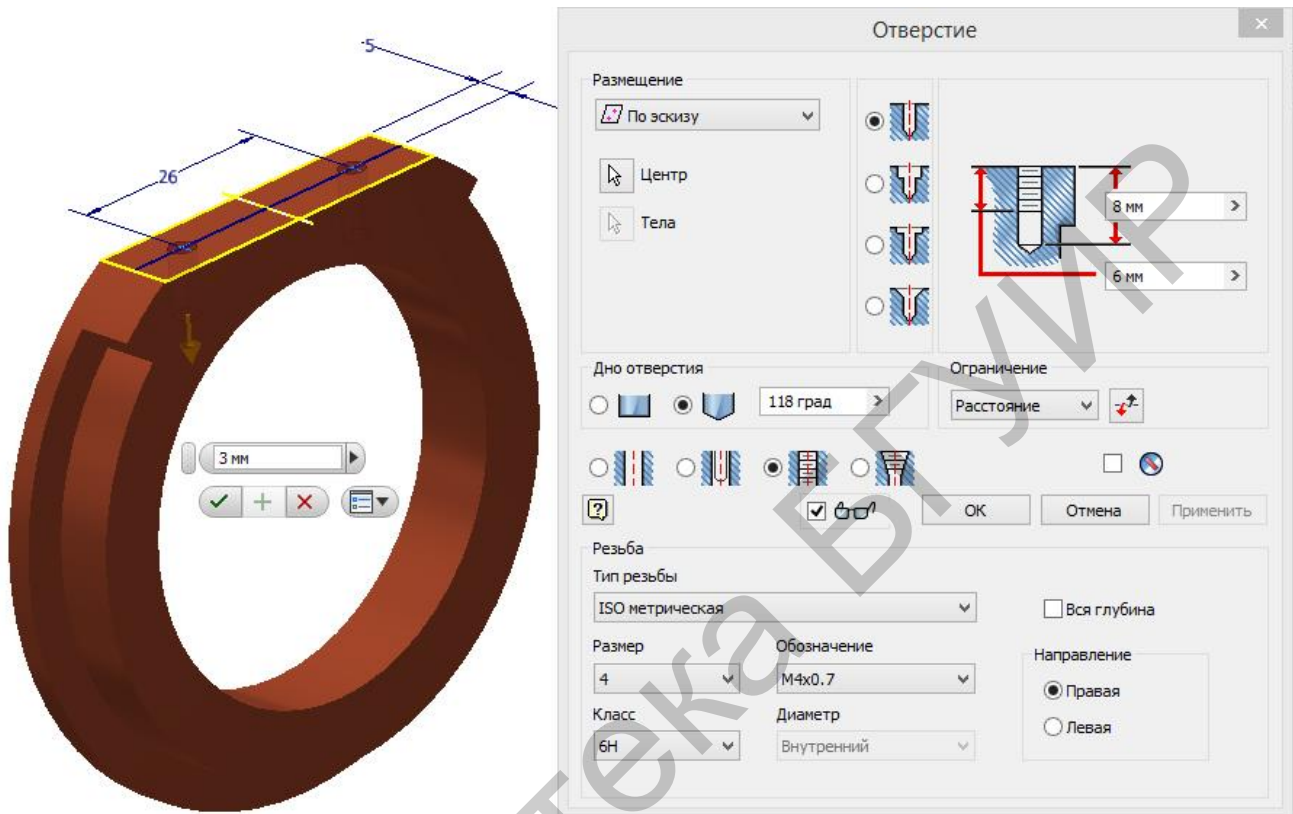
Выполнение двух глухих резьбовых отверстий М4 на поверхности среза
